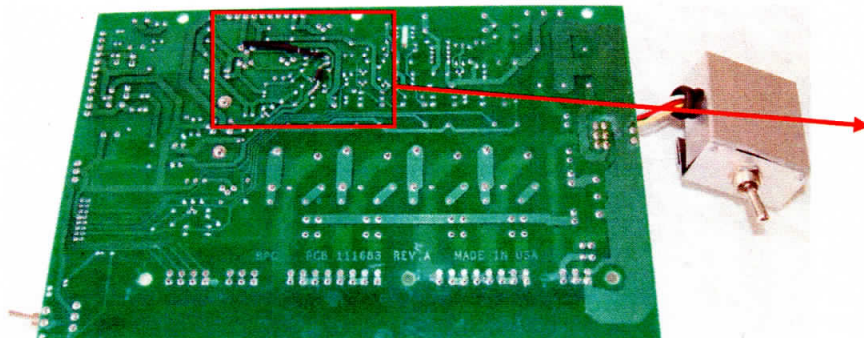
Detalle de pista cortada y dos diodos colocados por la cara de soldadura en la tarjeta Power Distribution Board Assembly con número de parte 116449 REV A.
